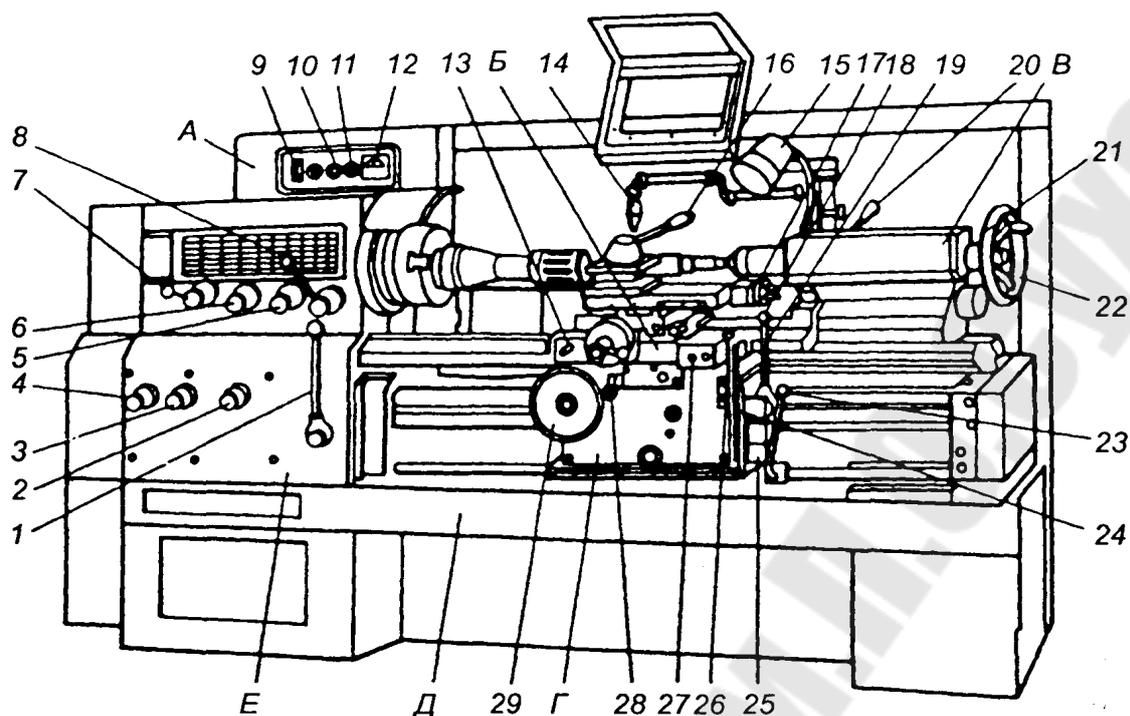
Общий вид токарно-винторезного станка: 1 — рукоятка управления фрикционной муфтой главного привода; 2 — вариатор подачи, шага резьбы и механизма отключения подачи; 3 — вариатор подачи и типа нарезаемой резьбы; 4 — вариатор подачи и шага резьбы; 5 — переключатель на левую, правую и другие резьбы; 6 — рукоятка установки нормального и увеличенного шага резьбы и положение при делении на ходы резьбы; 7, 8 — рукоятки установки частоты вращения шпинделя; 9 — вводный автоматический выключатель; 10 — лампа сигнальная; 11 — включение насоса СОЖ; 12 — указатель нагрузки станка; 13 — ручное перемещение поперечных салазок суппорта; 14 — регулируемое сопло СОЖ; 15 — освещение местное; 16 — рукоятка поворота и зажима резцедержателя; 17 — рукоятка перемещения верхних салазок суппорта; 18 — рукоятка включения двигателя ускоренного хода; 19 — рукоятка управления перемещения каретки и салазок суппорта; 20 — зажим пиноли задней бабки; 21 — рукоятка закрепления задней бабки на станине; 22 — маховик перемещения пиноли задней бабки; 23, 24 — рукоятки включения и отключения муфты главного привода; 25 — включение подачи; 26 — винт закрепления каретки на станине; 27 — кнопочная станция двигателя главного привода; 28 — рукоятка включения и выключения ременной шестерни; 29 — маховик ручного перемещения каретки.
